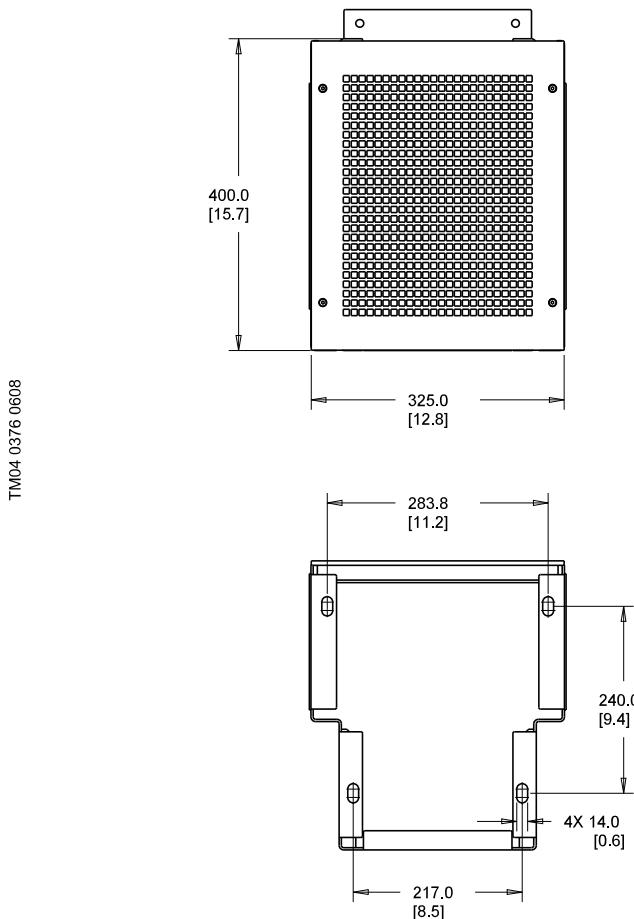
Шаблон для сверления под цоколь D1h (мм)
